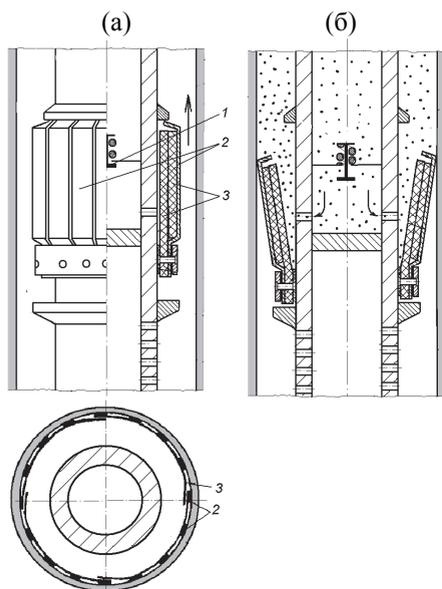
Конструкция пакера: пакер при спуске в скважину (а); положение пакера при цементации (б); 1 – обратный клапан; 2 – защитные пластины; 3 – эластичные сектора
